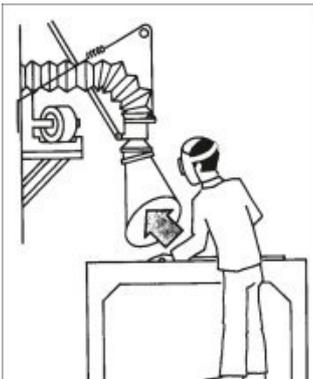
Flexible Punktabsaugung, so genannter Elefantenrüssel, z.B. beim Schweißen
